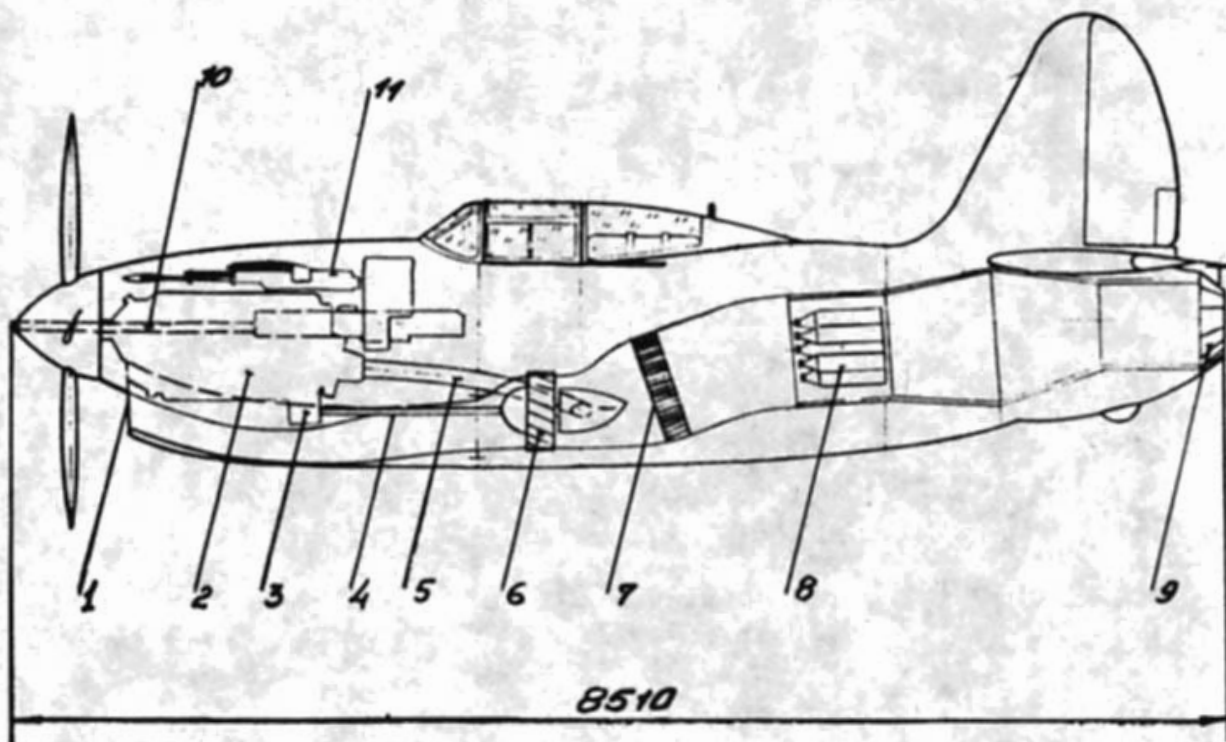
Компонировка компрессорного воздушно-реактивного двигателя на самолете И-107 (Су-5):
